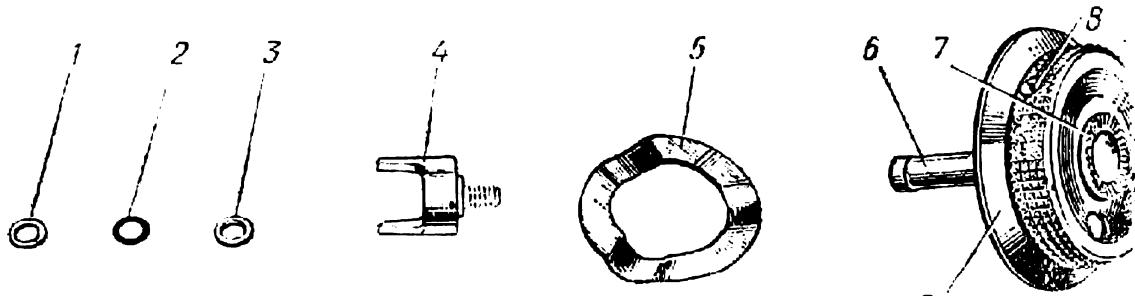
Детали механизма перемотки фотоаппарата «Киев-4А»:
